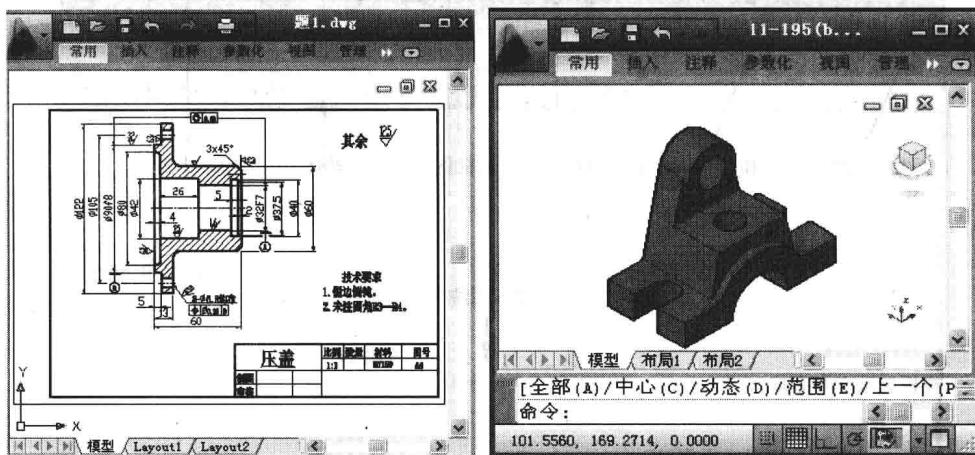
利用 AutoCAD 绘制的二维零件图和实体零件图
